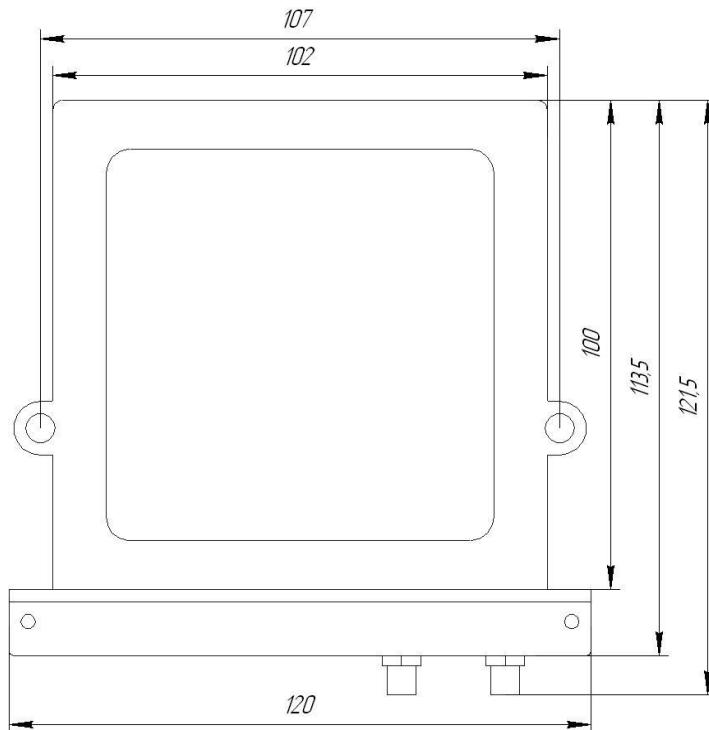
Внешний вид и габаритные размеры Радиотерминала «BI 864 TREK V.2». (Вид сверху)
